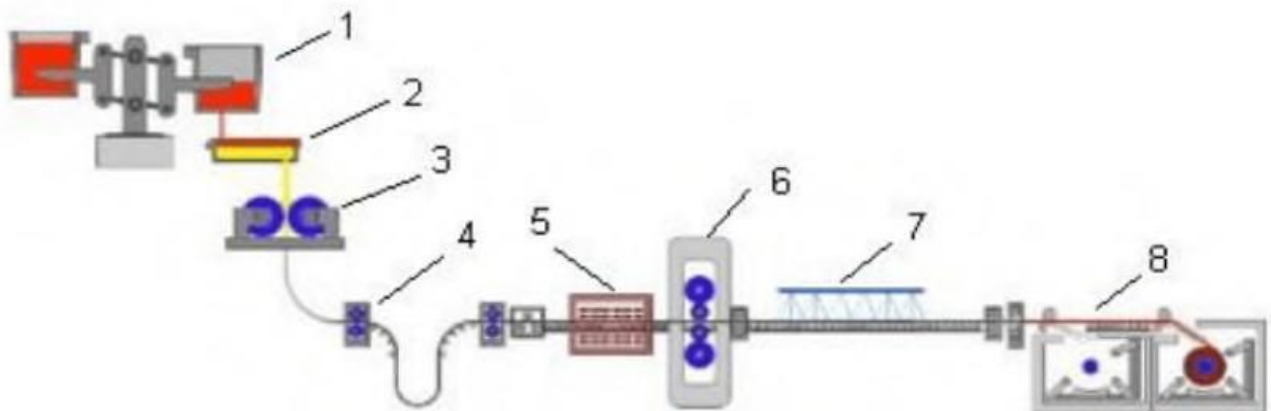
Схема валкової розливки-прокатки: 1 – сталерозливний ківш; 2 – проміжний ківш; 3 – валки-кристалізатори; 4 – тягнучі ролики; 5 – індукційна піч; 6 – чотиривалкова прокатна кліть; 7 – установка прискореного охолодження металевго сплаву; 8 – моталки
